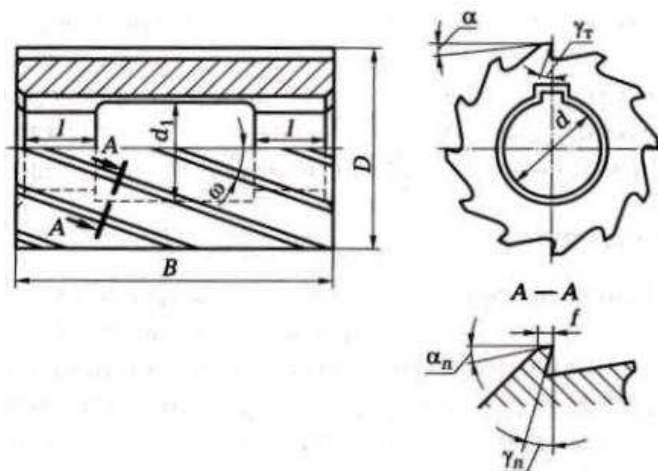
Конструктивные и геометрические параметры цилиндрической фрезы: D — диаметр фрезы; B — ширина фрезы; d — диаметр посадочного отверстия; d_1 — диаметр выемки; α — задний угол; γ_r — передний угол в торцовом сечении; α_n и γ_n — соответственно задний и передний угол в сечении по нормали к режущей кромке
